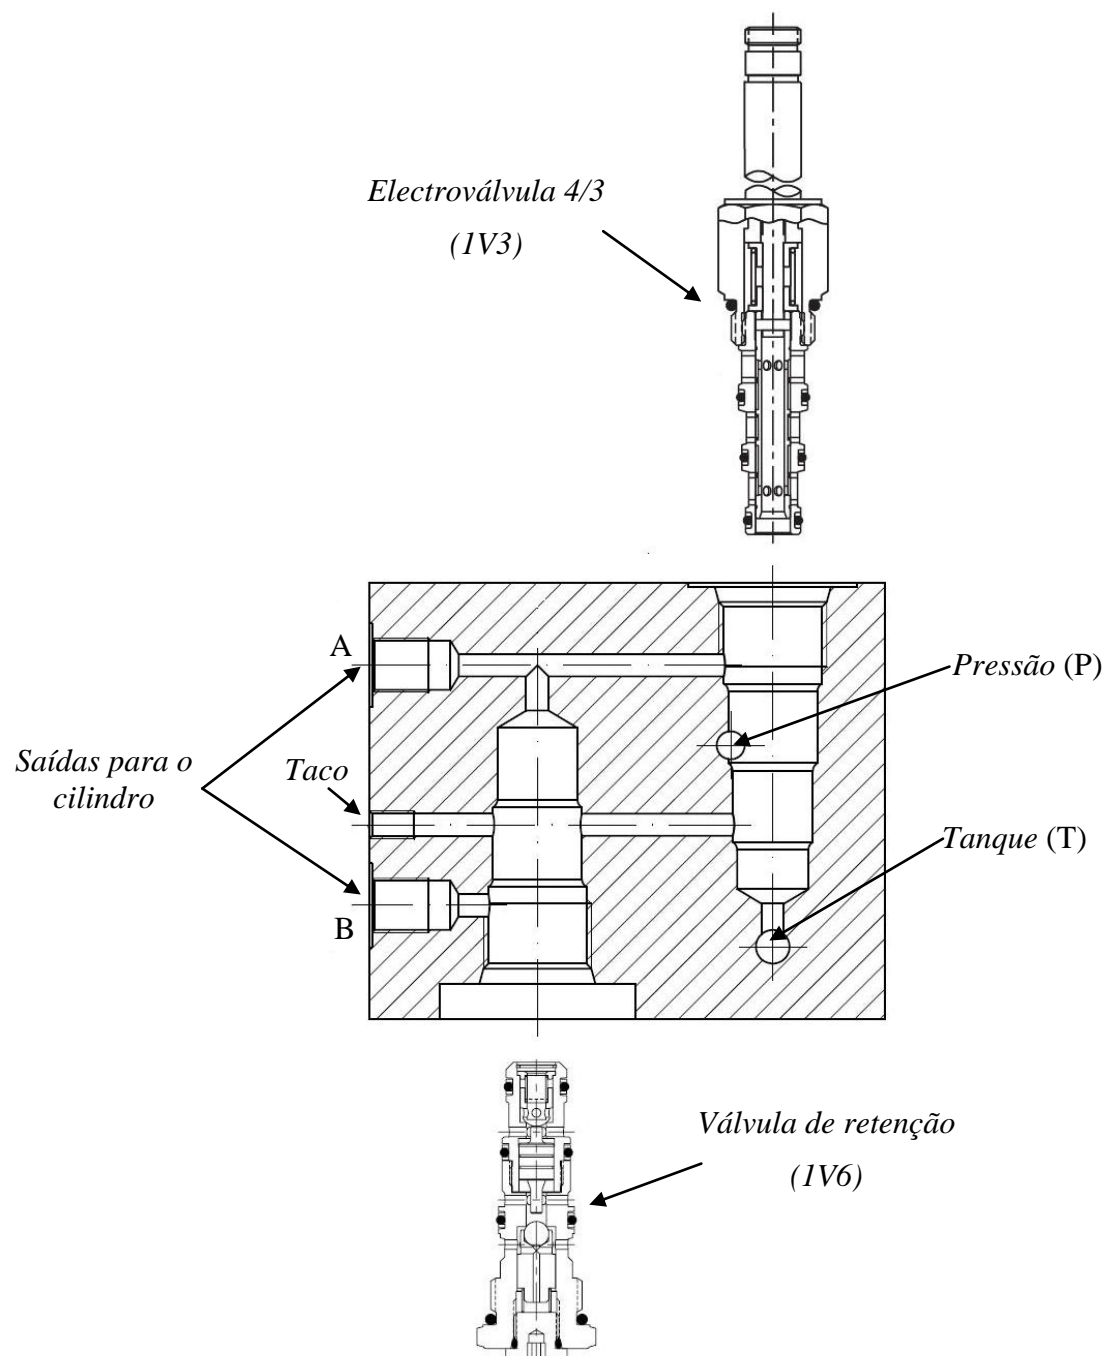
Vista em corte com as válvulas de comando do cilindro da elevação
